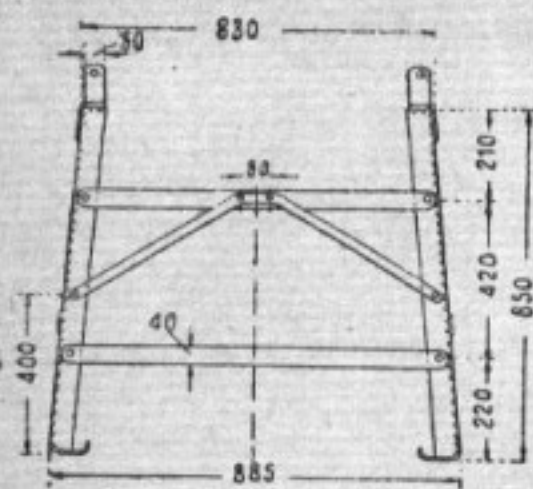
Стенд для демонтажа и монтажа передних мостов ГАЗ-АА
